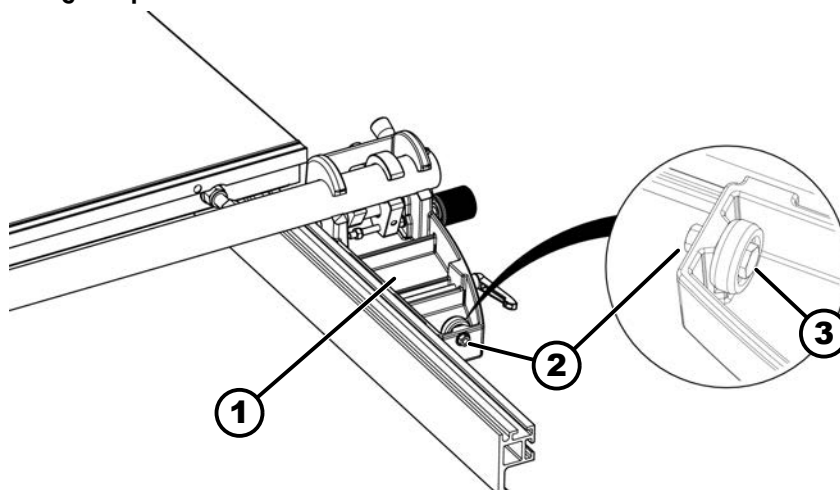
Ajuster la hauteur du guide de coupe parallèle
